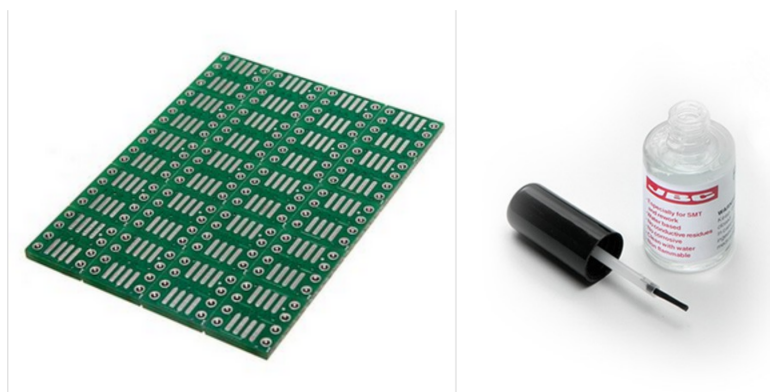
A la izquierda la placa empleada para la soldadura de los LEDs, a la derecha el flux empleado en las soldaduras (BJC FL-15)
